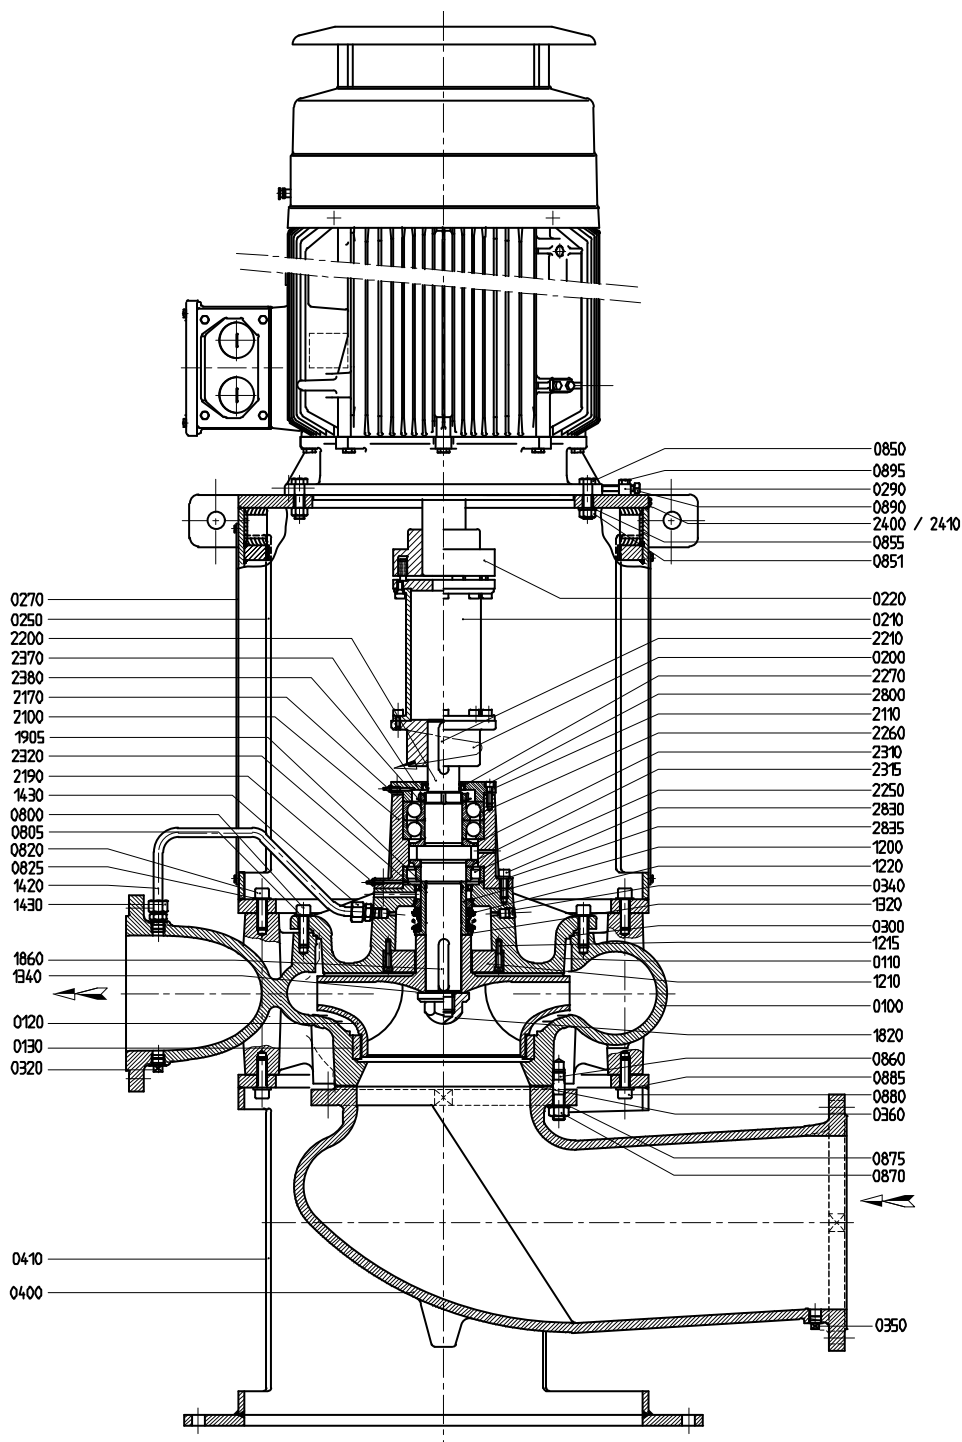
Чертеж в разрезе 200–400, 250–250, 250–315, 300–250, 300–315.
